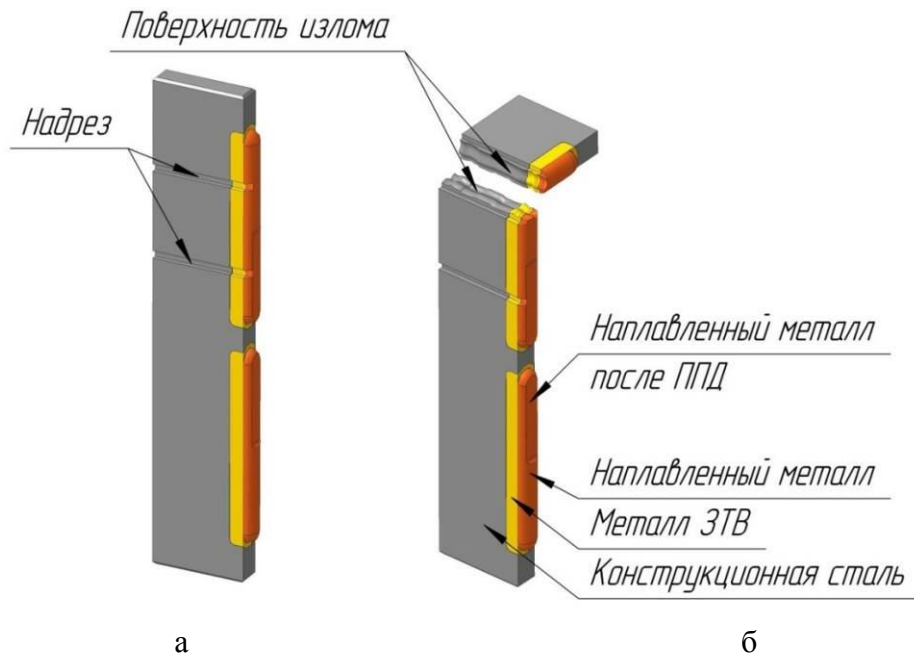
Схема получения изломов: а – надрез образца; б – проведение излома полосы
